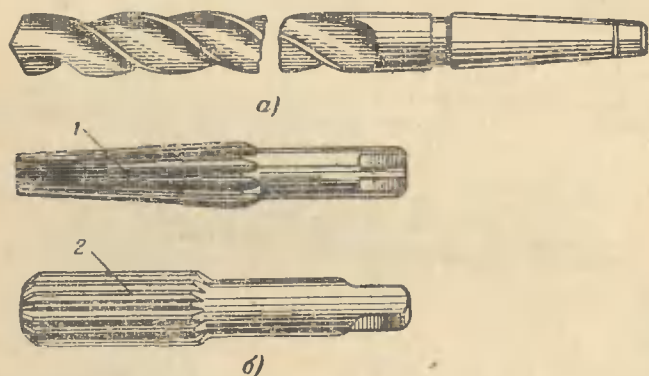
Инструменты для сверления и обработки поверхностей круглых отверстий.
